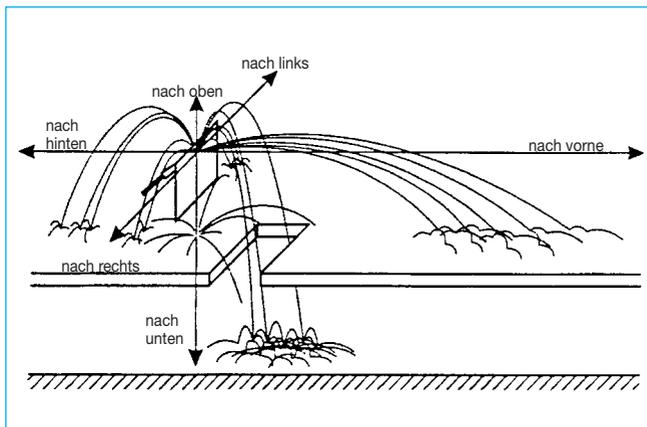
Ausbreitungsverhalten heißer Partikel bei schweißtechnischen Arbeiten
